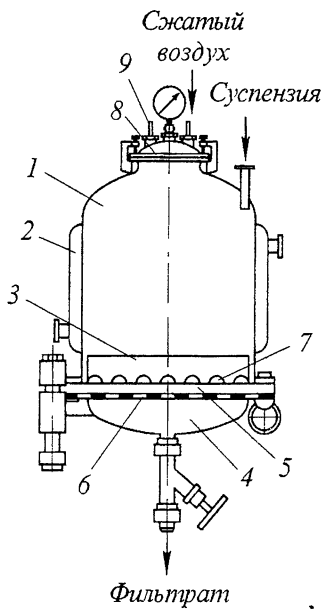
Друк-фильтр: 1 — корпус; 2 — обогревающая рубашка; 3 — кольцевая перегородка; 4 — откидывающееся дно; 5 — фильтровальная перегородка; 6 — опорная решетка; 7 — сетка; 8 — съемная крышка; 9 — предохранительный клапан
